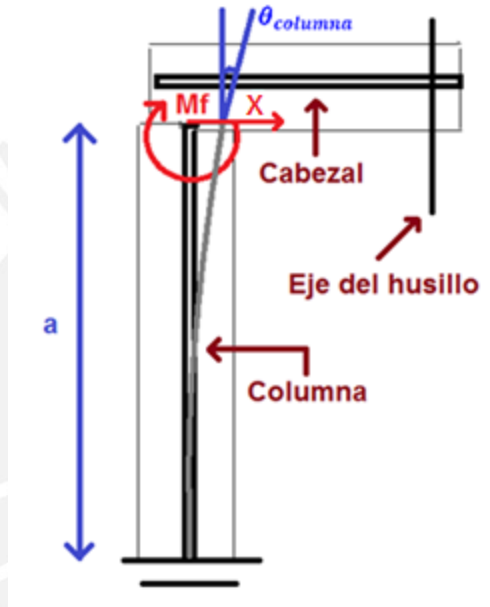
Esquema de la columna como viga en voladizo, donde $a=1200 \text{ mm}$
